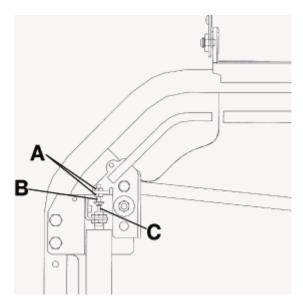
Réglage du dossier du relève-buste pneumatique 5051
